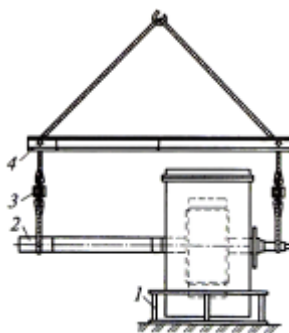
Пристрій для виведення ротора електричних машин 15...19 габаритів: 1 – плита; 2 – подовжувач; 3 – регулювальний болт; 4 – траверса
